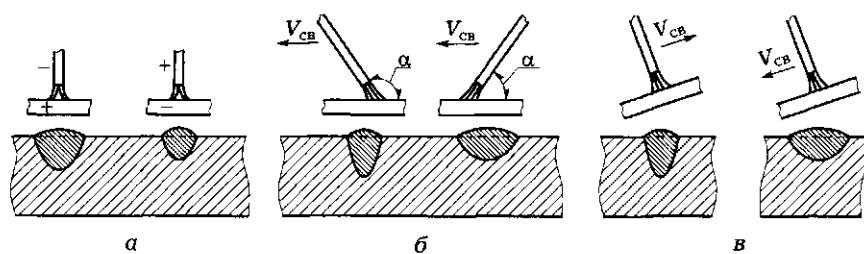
Формы сварных швов при сварке на постоянном токе прямой или обратной полярности (а), сварке углом α назад или углом вперед (б), при отклонении поверхности детали от горизонтальной плоскости (в)
